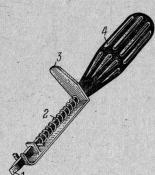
1 — лезвие - (стержень); 2 — пружина; 3 — лапка; 4 — ручка
